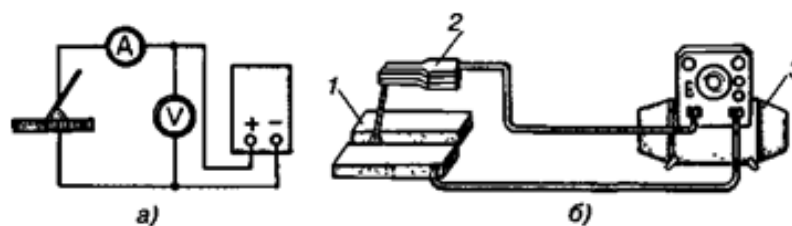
Схема поста ручной дуговой сварки покрытыми электродами: а) - электрическая сварочная цепь, б) - компоновка сварочного поста, 1 – деталь 2 – держатель, 3 – источник питания дуги
